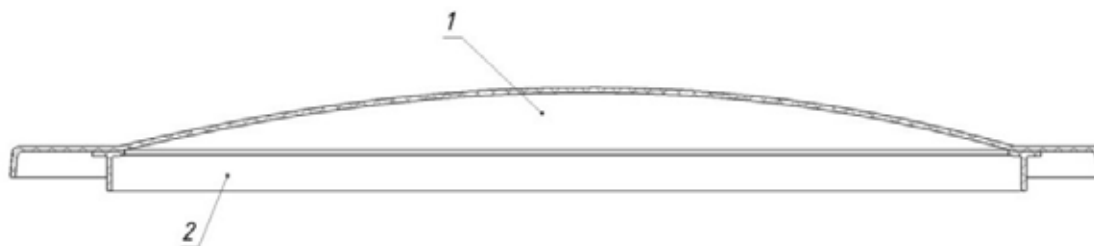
Формообразующая часть оправки: 1 — формообразующая оболочка со вспомогательной поверхностью и отбортовкой, 2 — ребро жесткости
